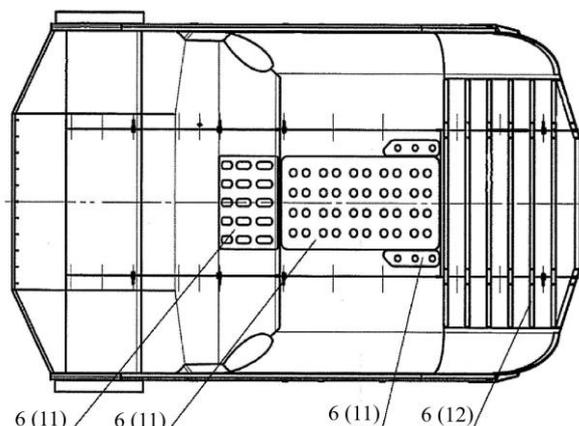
Футеровка пластинчатыми элементами (RU216348U1)
